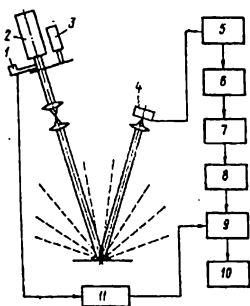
Контроль шорсткості поверхні з використанням лазерного проміння:
